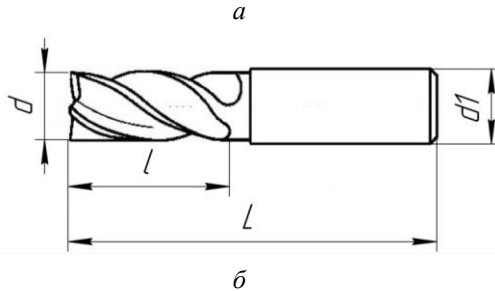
Обрана твердосплавна фреза 11-1-А-1-12-83;
